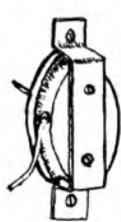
Vorschlag für die Befestigung des Kopfhörerkapsels am Chassis.
